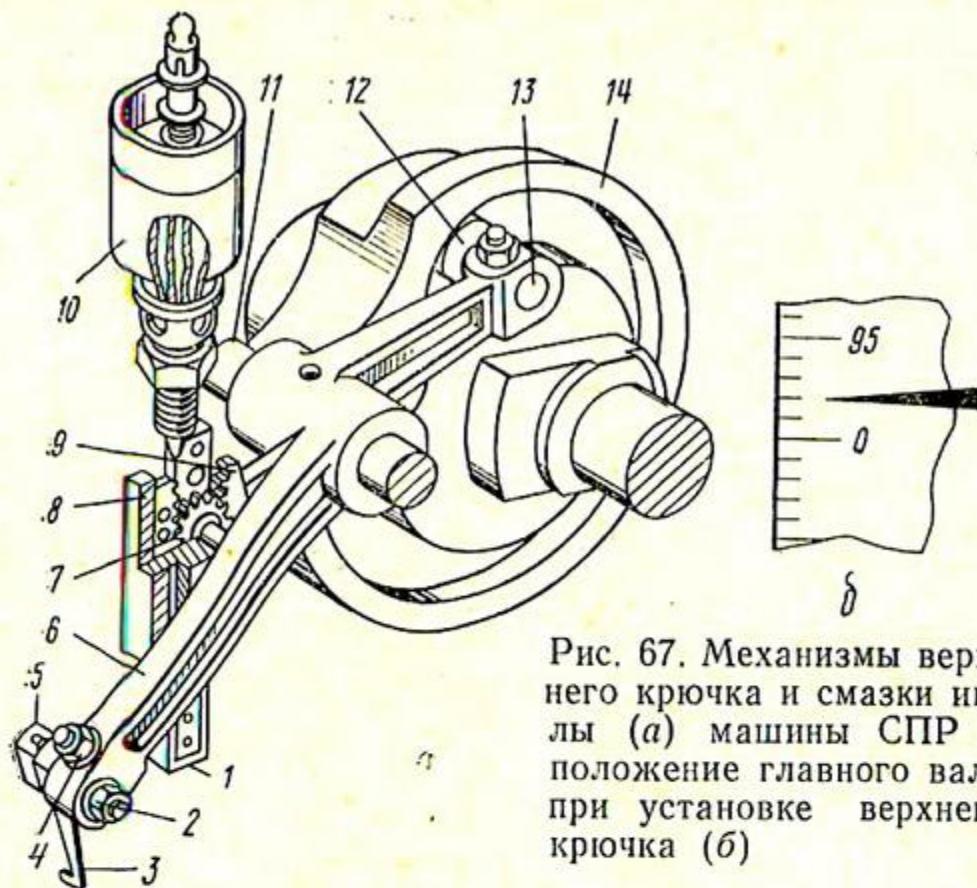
Механизмы верхнего крючка и смазки иглы (а) машины СПР и положение главного вала при установке верхнего крючка (б)
